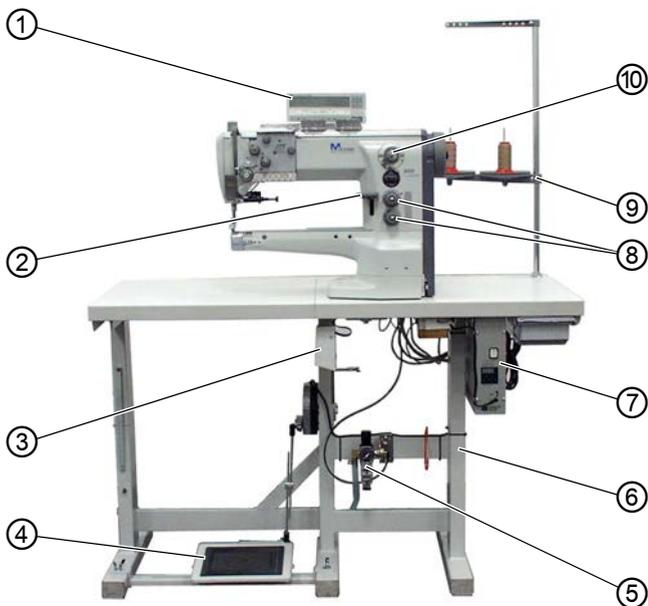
Componentes de la máquina (1), con bastidor MG 55-3
